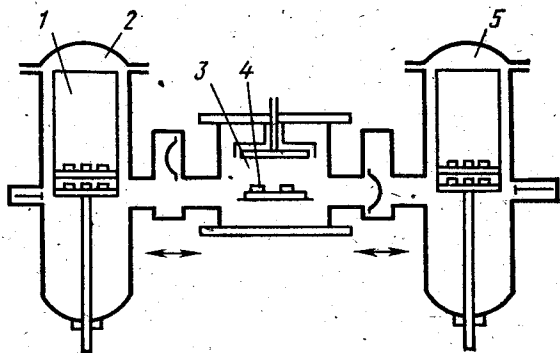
Установка полунепрерывного действия линейной компоновки с двумя шлюзовыми загрузочно-выгрузочными камерами:
